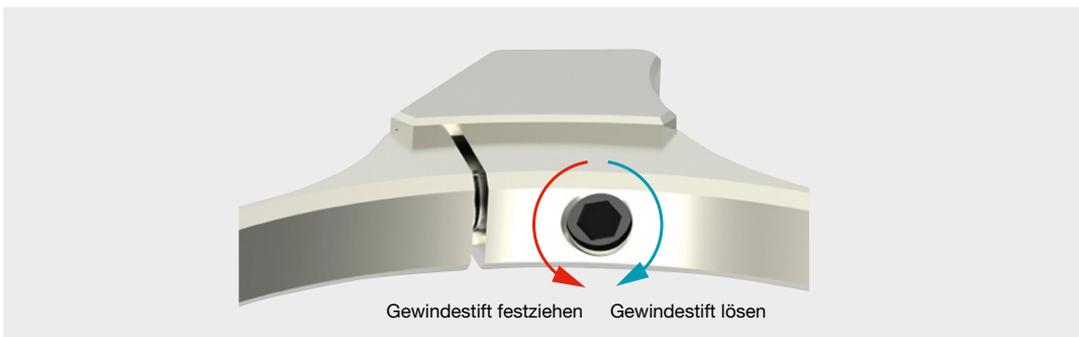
Drehrichtung für Befestigen und Lösen des Gewindestiftes
